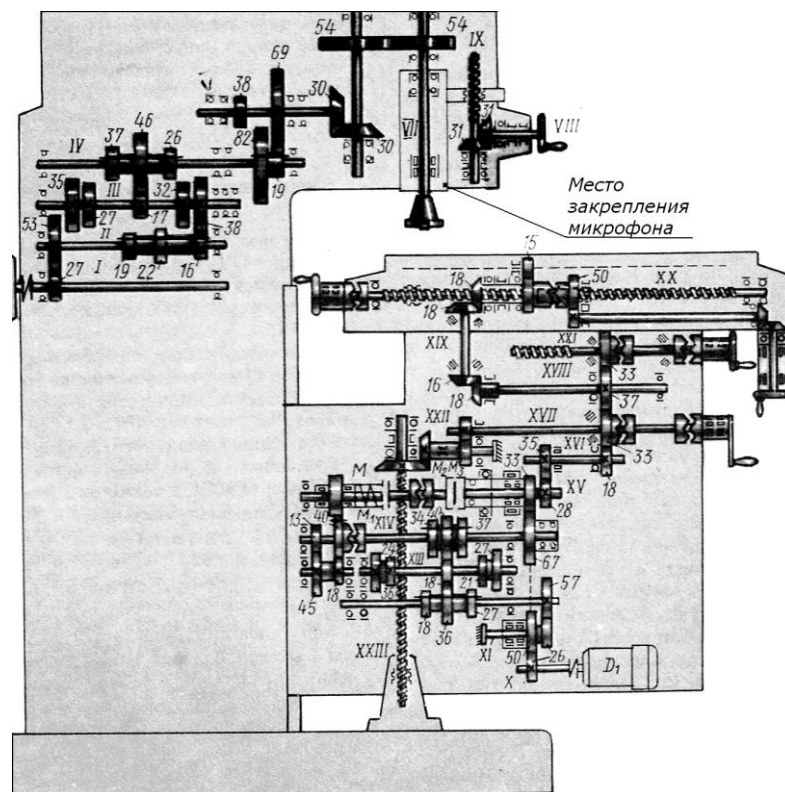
Кинематическая схема фрезерного станка 6P13 с указанием места закрепления микрофона
